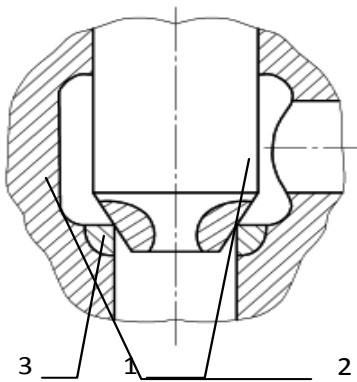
Традиційна конструкція метал-металевого затвора з демпфіруванням через пружну деформацію елементів: 1 — золотник, 2 — сідло, 3 — корпус
